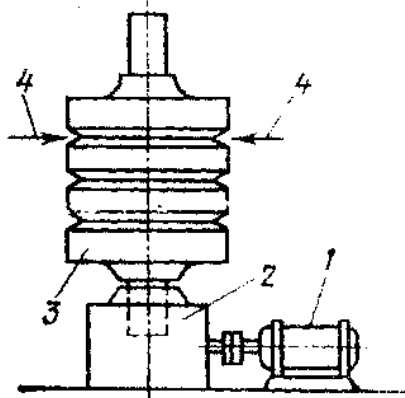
Схема зварювання ротора газової турбіни
